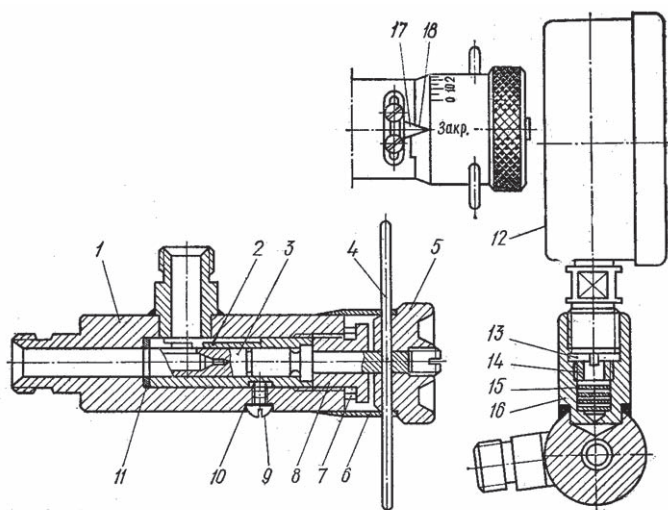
Витратомір КИ-5473: 1 — корпус; 2 — гільза; 3 — плунжер; 4 — стержень; 5 — рукоятка дроселя; 6 — лімб; 7, 10, 11, 13 — ущільнювальні прокладки; 8 — упорна гайка; 9 — установочний гвинт; 12 — манометр; 14 — спеціальна гайка; 15 — шайба демпфера; 16 — корпус; 17 — обмежувач; 18 — стрілка.
